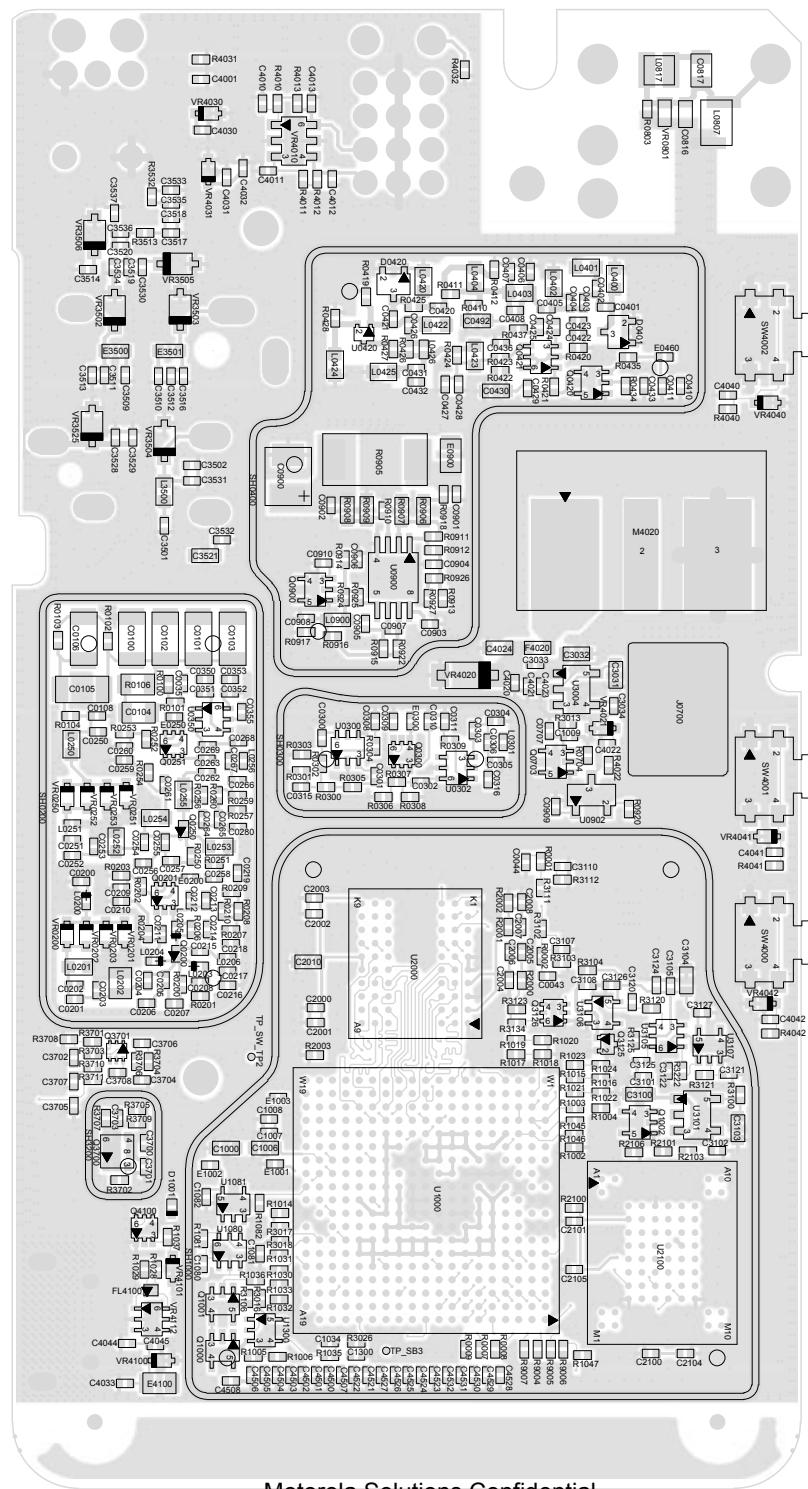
PCB da Parte Inferior da Placa Principal Nº PC002091A01_AA
